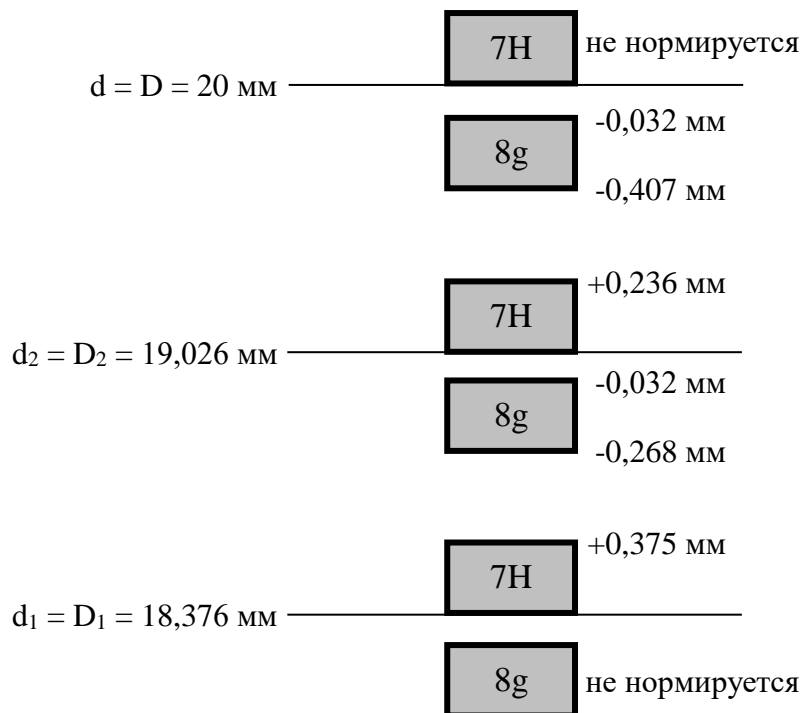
Схема расположения полей допусков резьбового соединения.
